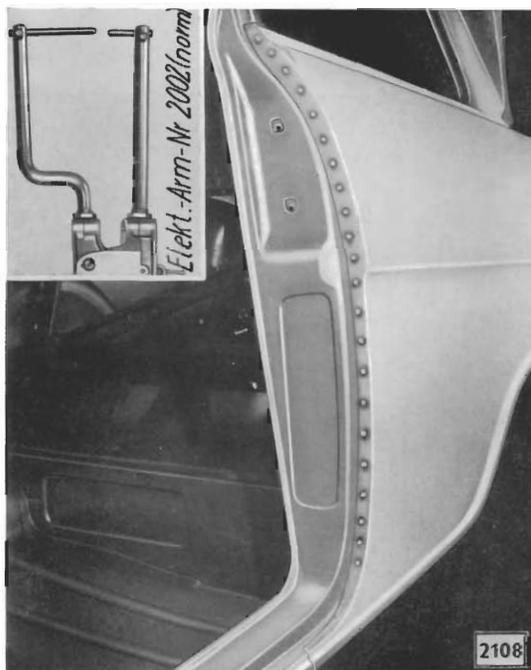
Seitenwand an Karosserieschloßsäule zangenpunktgeschweißt
